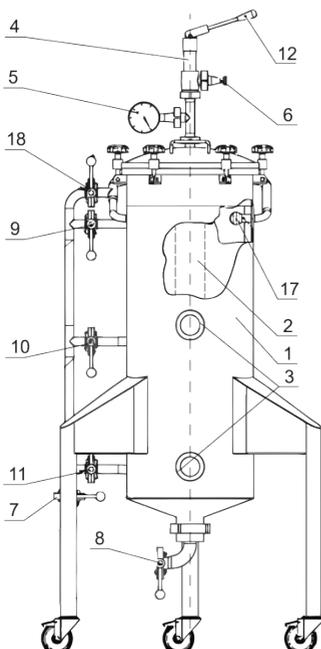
Схема установки для сухого охмеления пива: 1 – вертикальная цилиндрическая емкость на роликовых опорах; 2 – сетчатый сепаратор; 3 – смотровой диоптр; 4 – предохранительный клапан с рычагом сброса давления; 5 – манометр с мембранным разделителем; 6 – кран подачи углекислоты; 7 – кран входа и 8 – выхода пива; 9–11 кран тангенциального входа; 12 – воздуховыпускный рычаг; 17 – трубопровод CIP с двумя моющими головками; 18 – кран CIP мойки; 19 – насос
